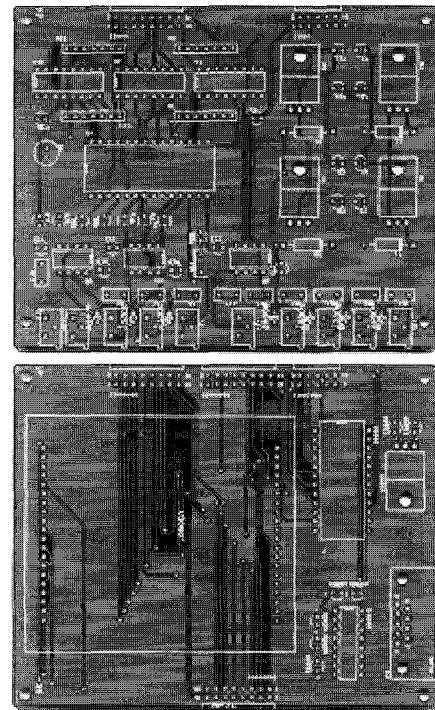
(a) 스트레인 게이지 센서 신호 증폭, 필터링, A/D 변환 회로도. PCB 기판 (b) 16 채널 전체 제어 회로도. PCB 기판.
